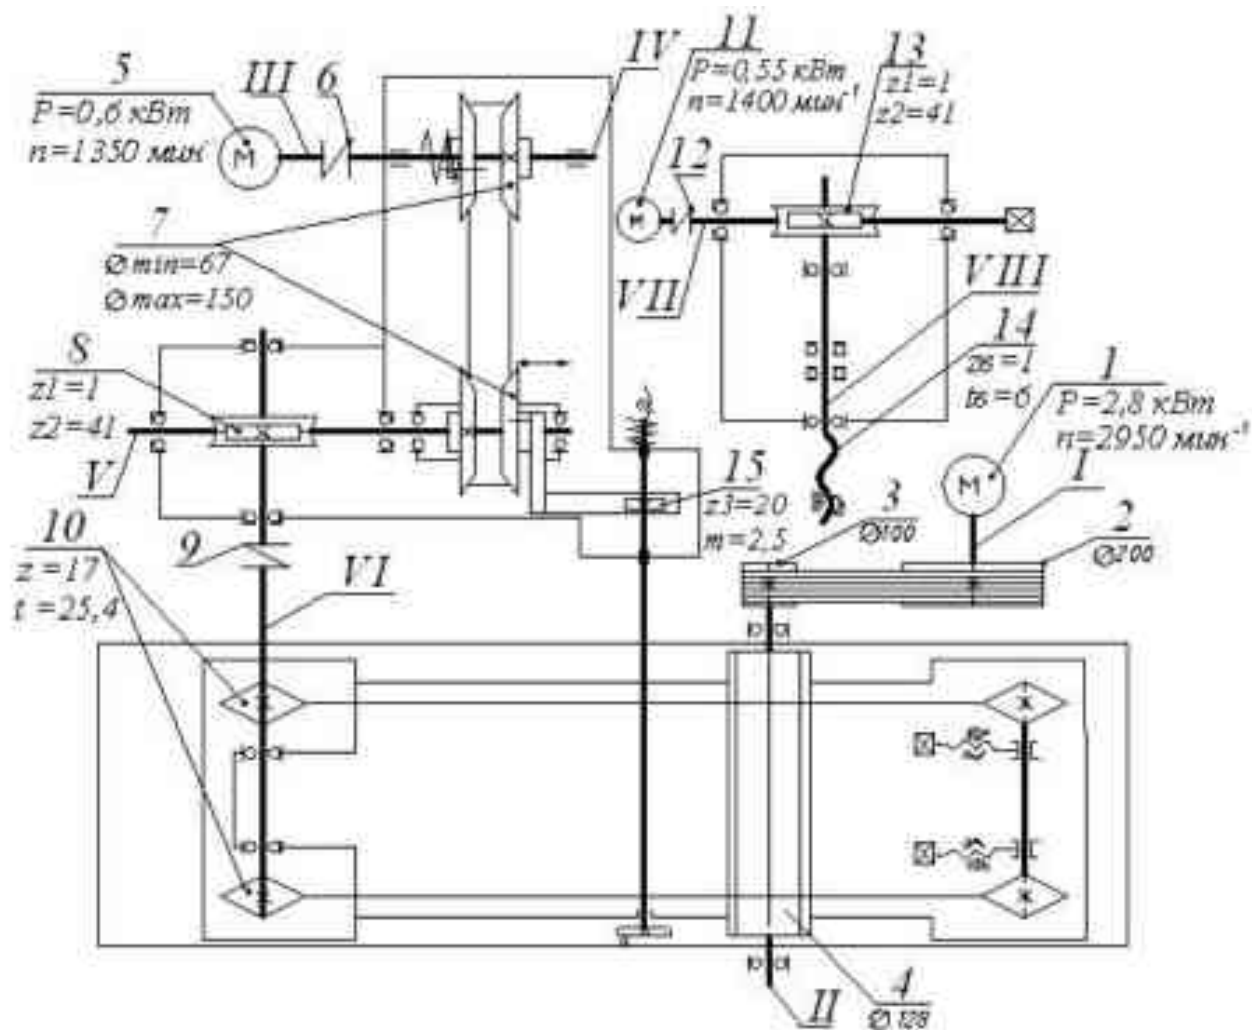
Схема фуговального станка с конвейерной подачей СФК4
